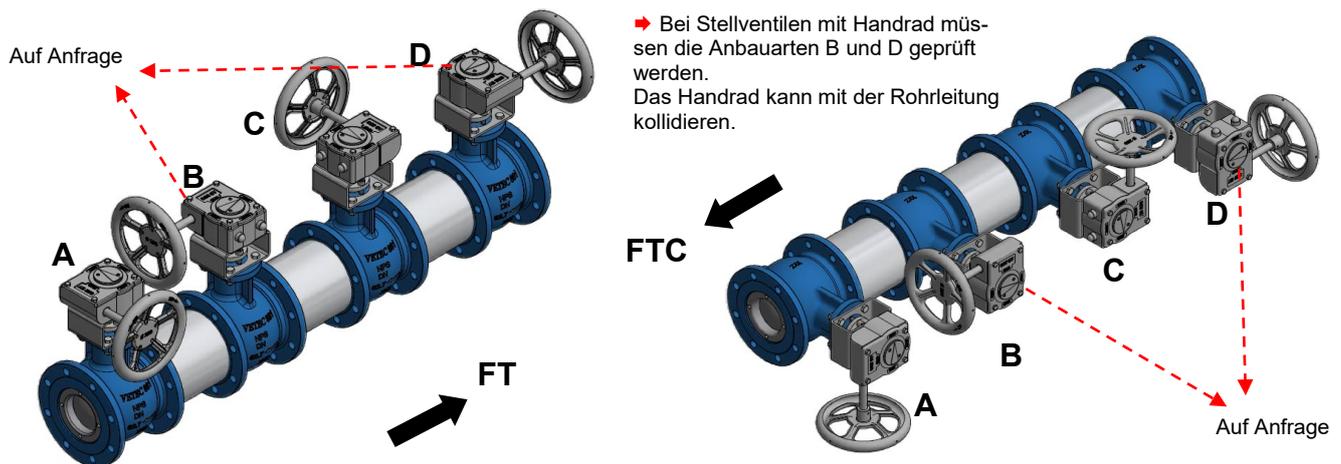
Stellventil Typ 62.7/AT-HR • horizontale Einbaulage • Anbauarten des Antriebs auf den Ventil A, B, C, D
